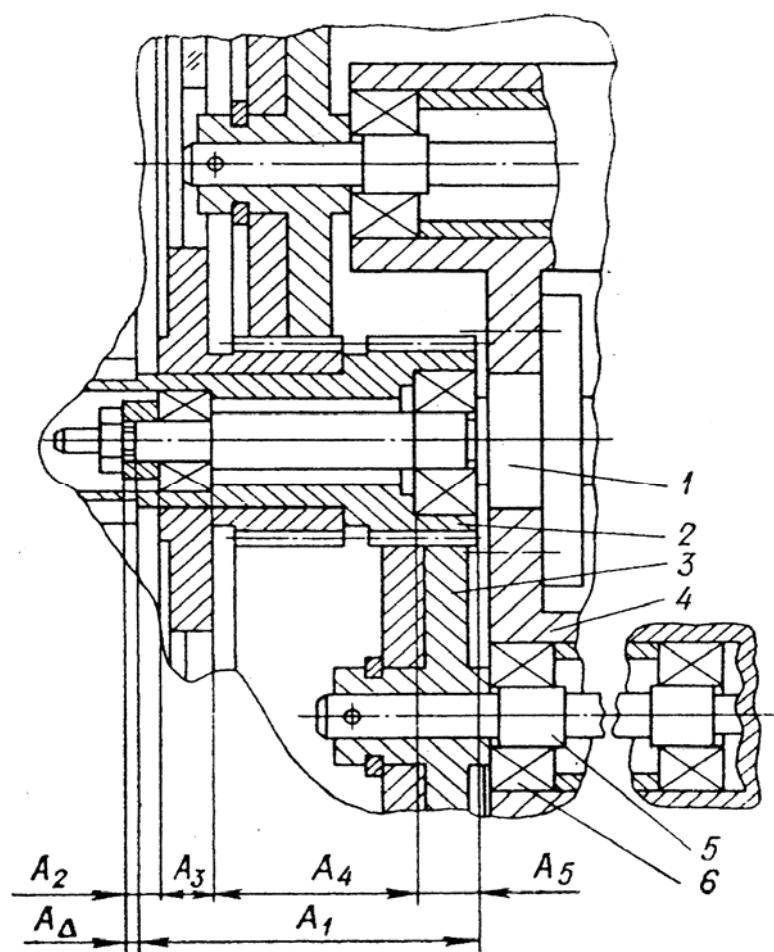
Узел подшипникового соединения: 1 – вал; 2 – колесо; 3- сателлит; 4 – водило; 5 – ось; 6 – подшипник
